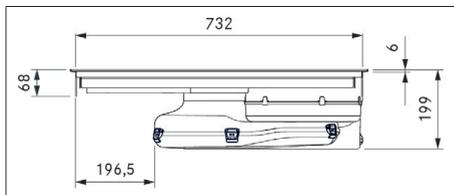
PURMU2/R dimensiones, vista frontal
